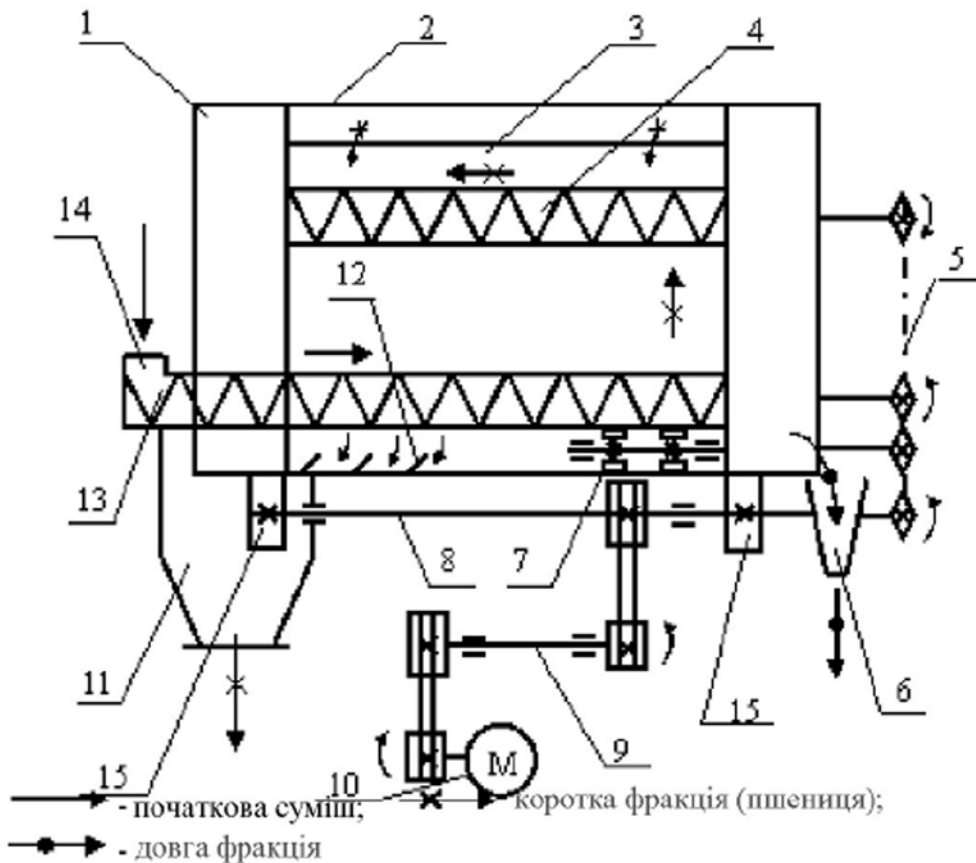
Схема ЦТ БТС 1 - бандаж; 2 - циліндр пористий; 3 - лоток; 4 - шнек для збору короткою фракції; 5 - передача ланцюгова; 6 - збірник вівсюга; 7 - зворошувач; 8 - вал приводних роликів; 9 - вал проміжний; 10 - електродвигун; 11 - збірник короткої фракції; 12 - плужок; 13 - шнек живильний; 14 - приймач; 15 - ролик привідний
